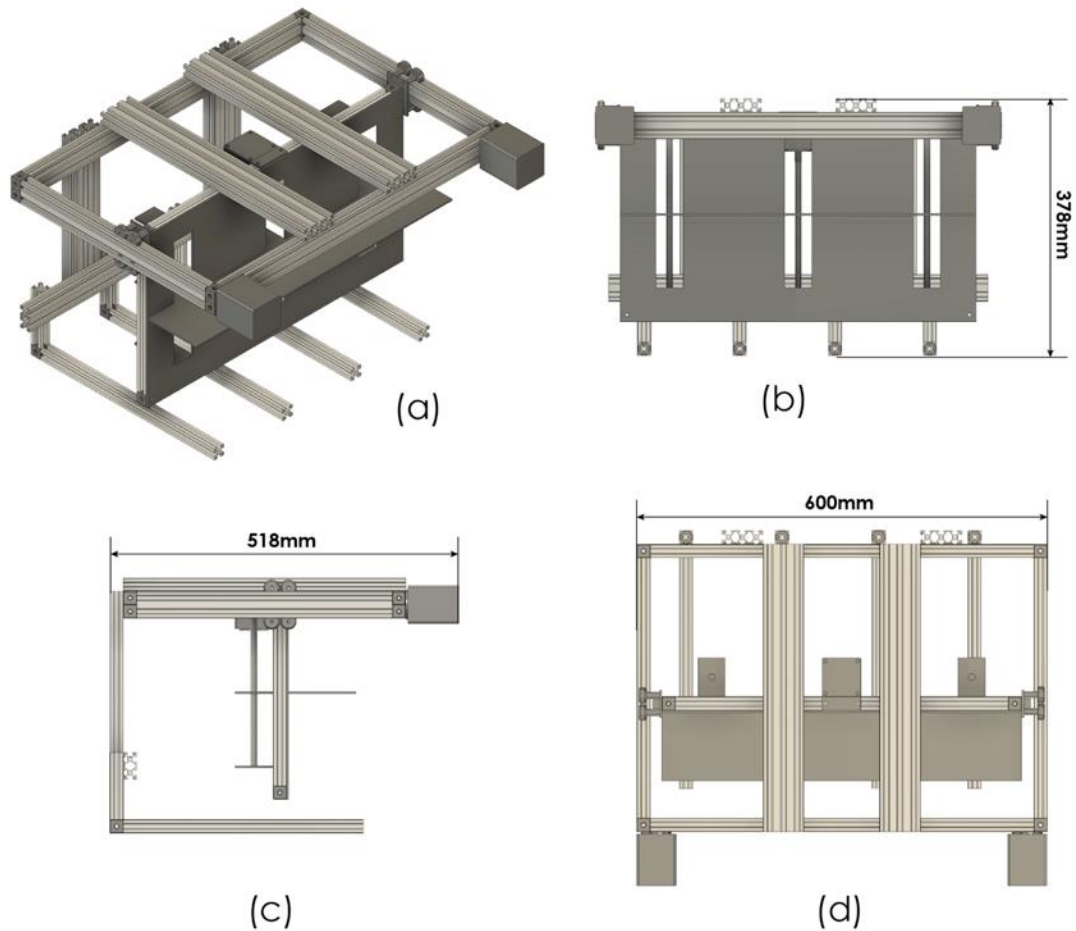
Vistas generales del gripper con dimensiones. (a) Vista isométrica. (b) Vista frontal. (c) Vista lateral. (d) Vista superior.
